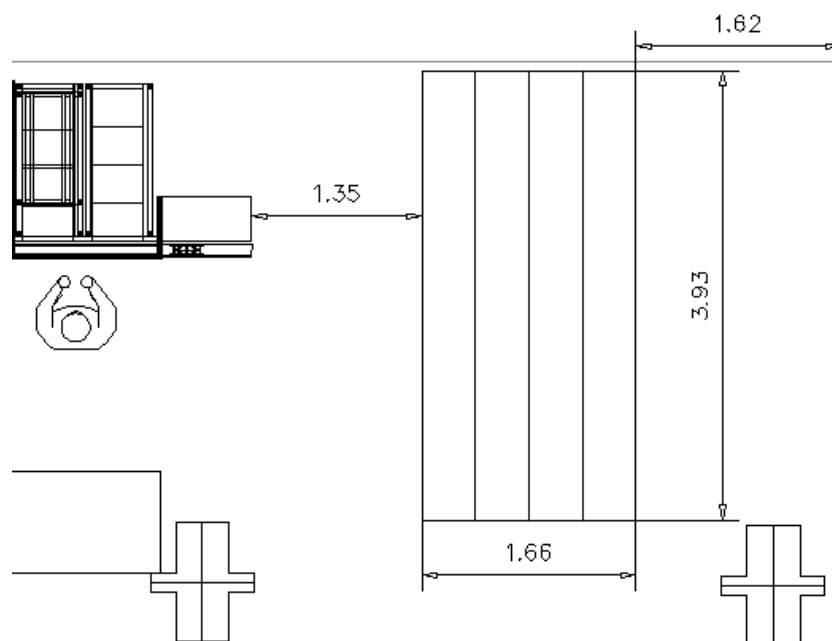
Extracto del Plano 3 - modificación de la Estantería SURYA
